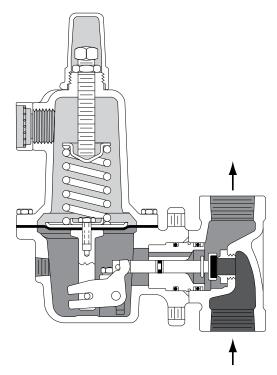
627W 型工作原理图 (也适用于 627WH 型)
